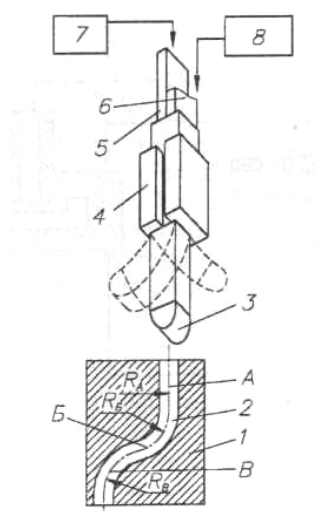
Схема устройства для электроэрозионной обработки отверстий с криволинейной осью: 1 – заготовка; 2 – обрабатываемое отверстие; 3 – рабочая часть электрода-инструмента; 4 – электрод-инструмент; 5 и 6 – гибкие поводки; 7 и 8 – механизмы изменения усилий на поводки
